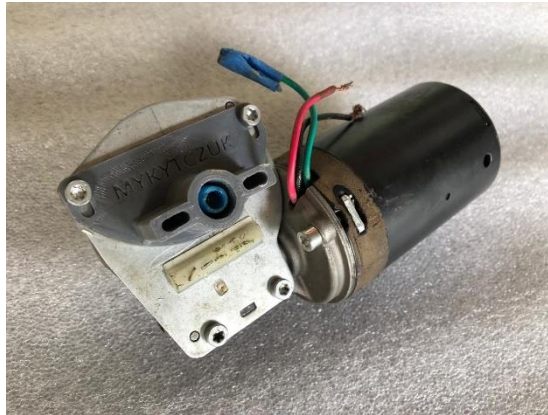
Parafuso preso a parte traseira da engrenagem do motor.
